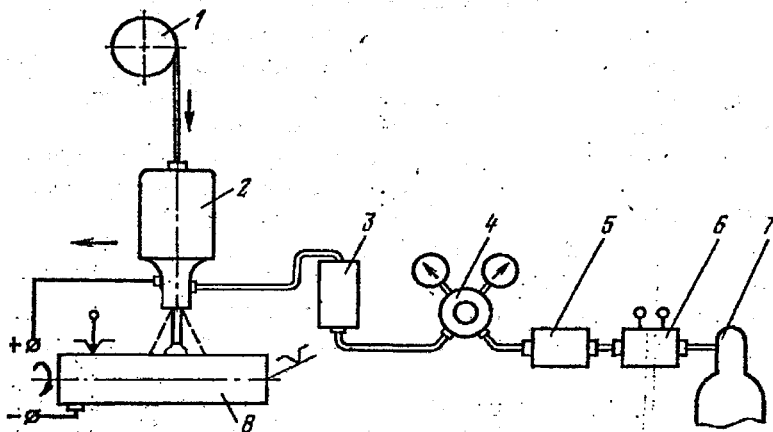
Принципова схема установки для электродугового наплавлення в середовищі вуглекислого газу: 1 – касета з дротом; 2 – наплавловальний апарат; 3 – ротаметр; 4 – редуктор; 5 – осушувач; 6 – підігрівник; 7 – балон із вуглекислим газом; 8 – деталь
